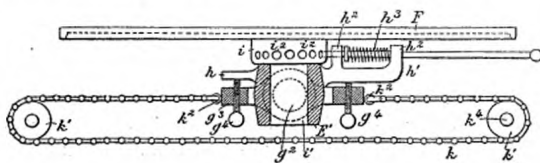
Vue de côté et en coupe du plateau qui reçoit la pièce à travailler.
